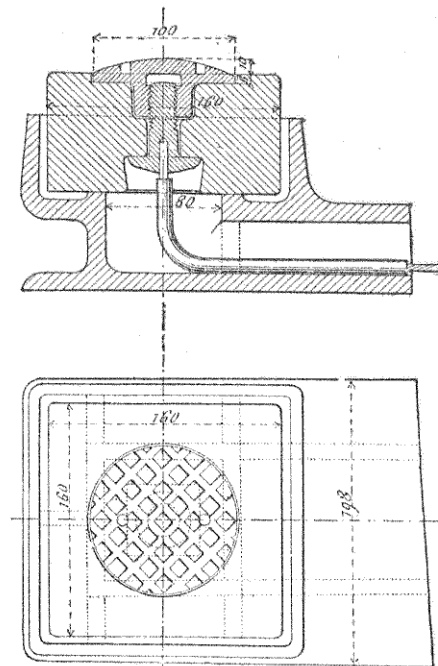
et 765. — Coupe et plan d'un plot pour tramways sur chaussée.
